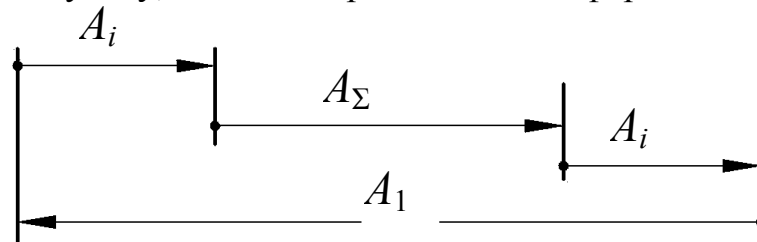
Схема розмірного лінійного ланцюга для оброблення напівкруглих канавок шліцьових валів
